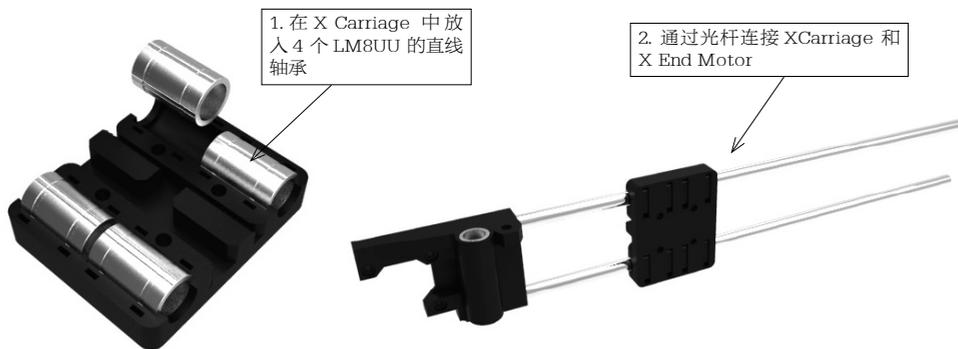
通过光杆连接 X Carriage 和 X End Motor
